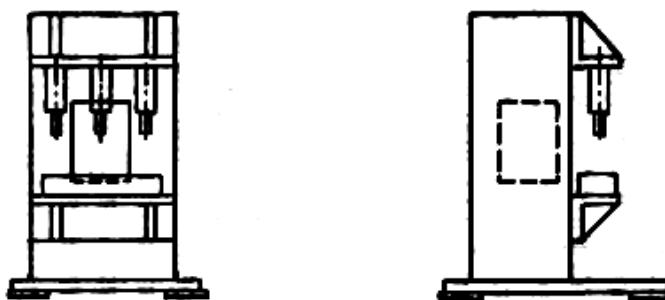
Многоэлектродная сварочная машина на базе С-образного пресса
